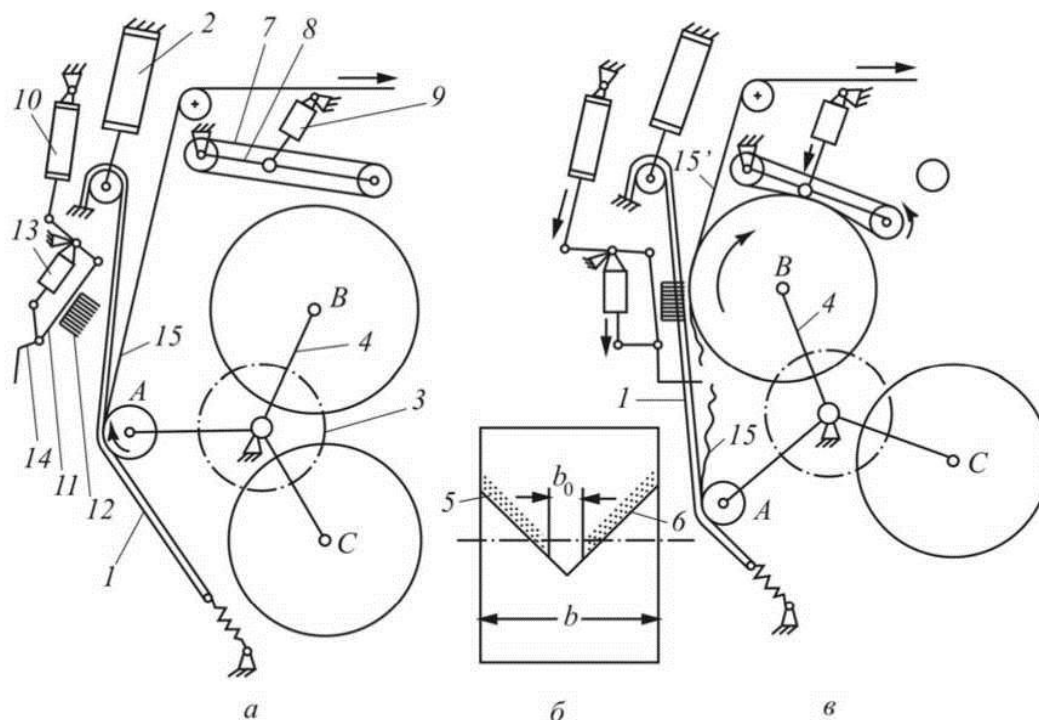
Схема автосклеивающего устройства: а - положение механизмов до начала склейки ленты; б - схема нанесения клея; в - положение механизмов в момент склейки лент; 1 - ременной тормоз; 2, 10, 13 - пневмоприводы; 3 - зубчатое колесо; 4 - луч; 5, 6 - кромка; 7 - бесконечный ремень; 8, 11 - рамы; 9 - гидропривод; 12 - щетки; 14 - ножи; 15 - лента
